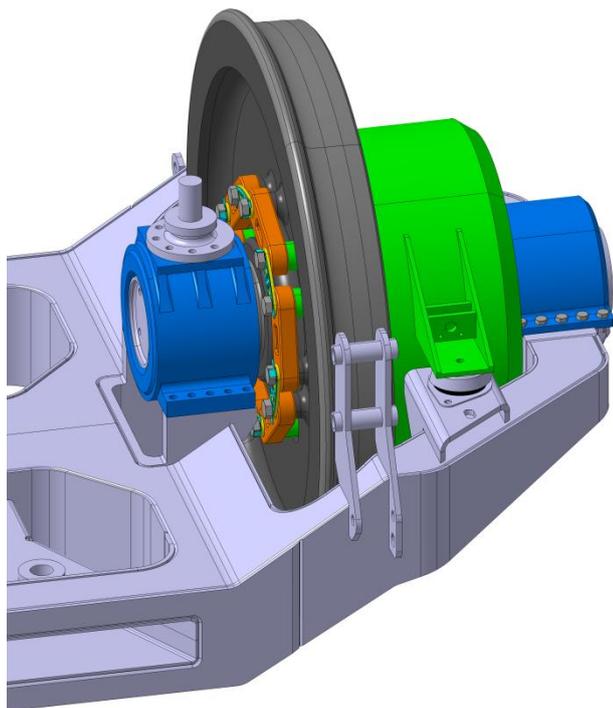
Detailansicht: Radträgerschweißbaugruppe mit Radbaugruppe
